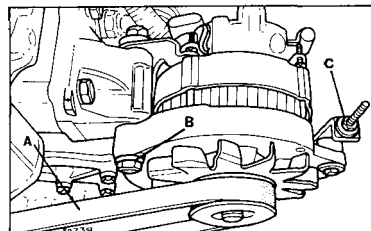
Проверка натяжения многоручьевого клиновидного ремня (A) и его регулировка, после ослабления болта (B) поворотом гайки (C)
